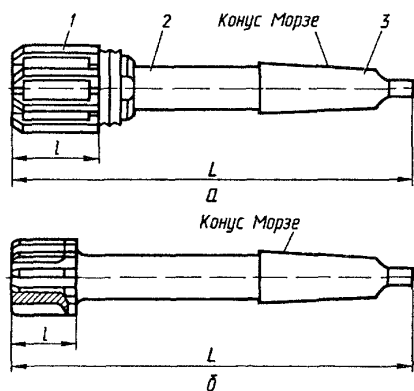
Машинні хвостові розвертки: а - регульована зі вставними ножами; б – твердосплавна; 1 - робоча частина; 2 – шийка; 3 - хвостовик; l - довжина робочої частини, L - загальна довжина розвертки
